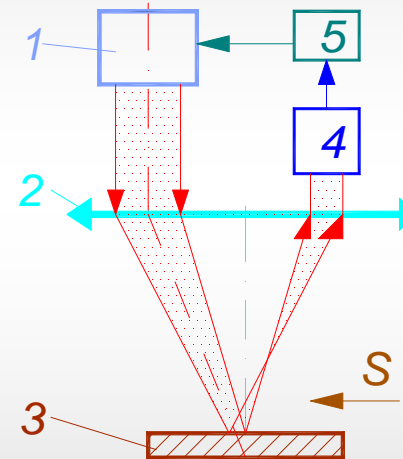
(13.13,14). Пристрій для лазерної обробки із стабілізацією процесу поглинання
